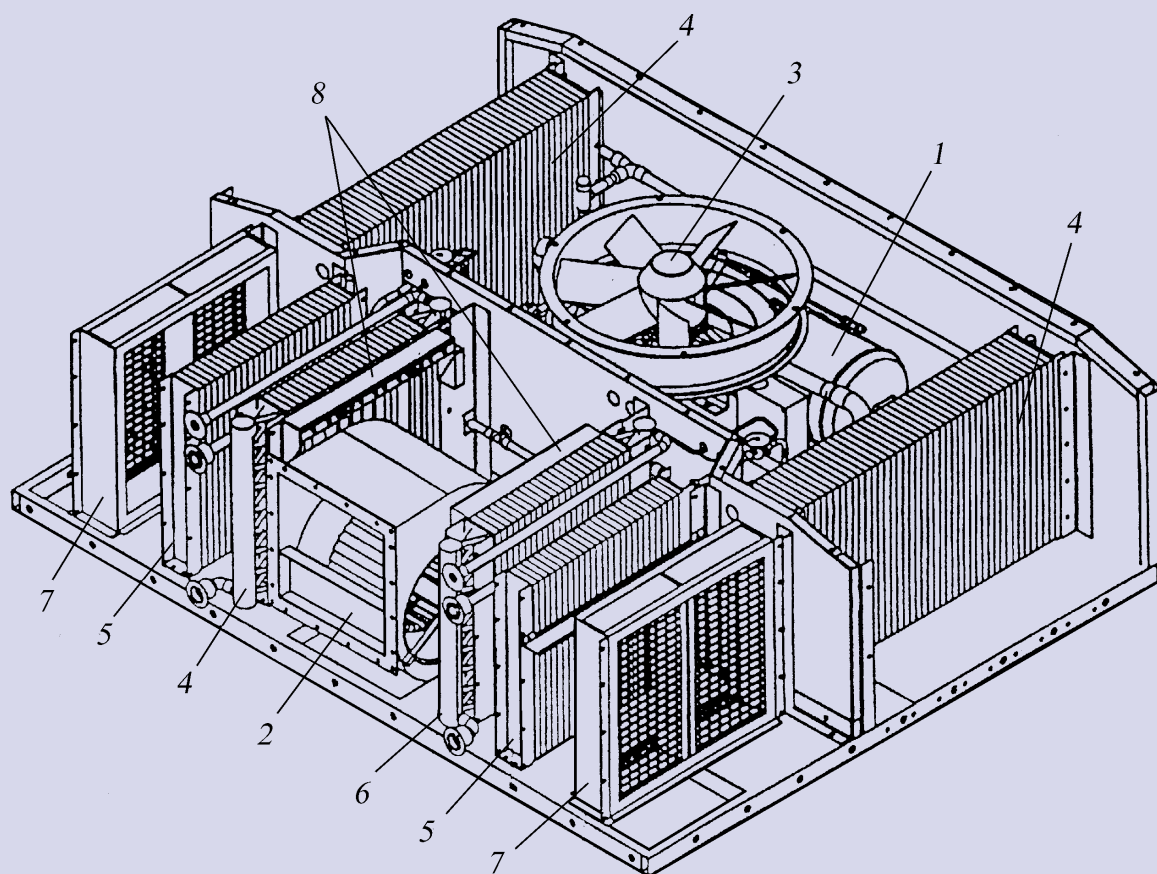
Компоновочная схема установки: 1 — компрессор; 2 — центробежный вентилятор; 3 — осевой вентилятор; 4 — конденсатор; 5 — воздухоохладители; 6 — водяные воздухонагреватели; 7 — фильтрующие ячейки; 8 — электрические воздухонагреватели
